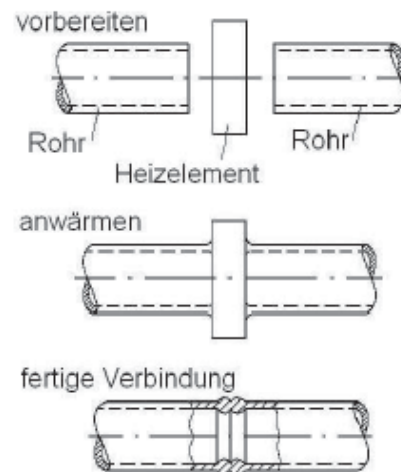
Prinzip des Hezelementstumpfschweißens am Beispiel Rohr.
